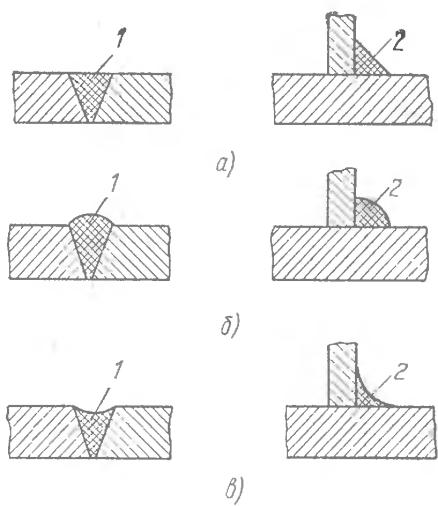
Классификация сварных швов по форме внешнего контура сечения шва:
